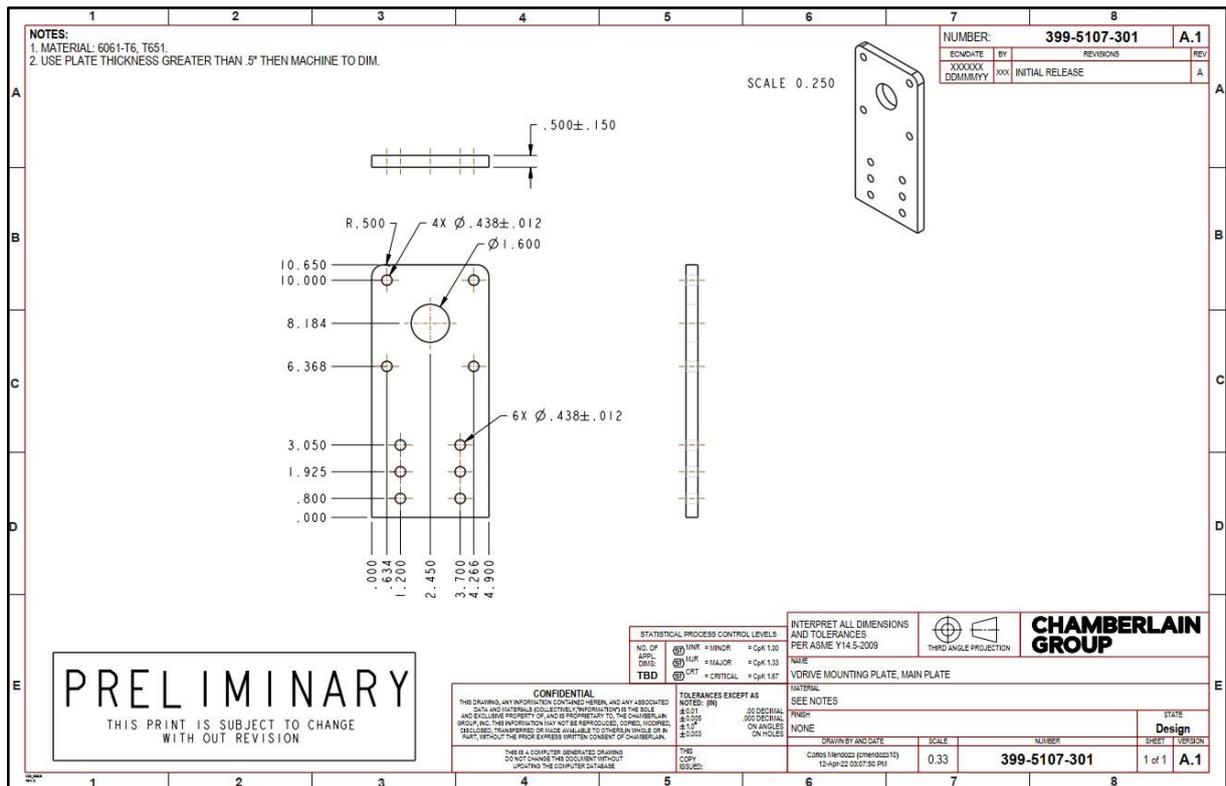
Plano de manufactura preliminar de la pared de montaje para VDrive
